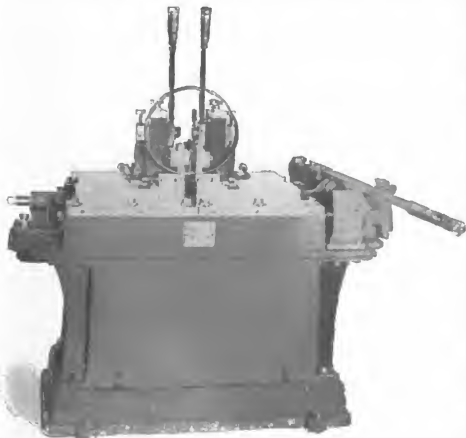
Reifenschweissmaschine Type 20 A.
